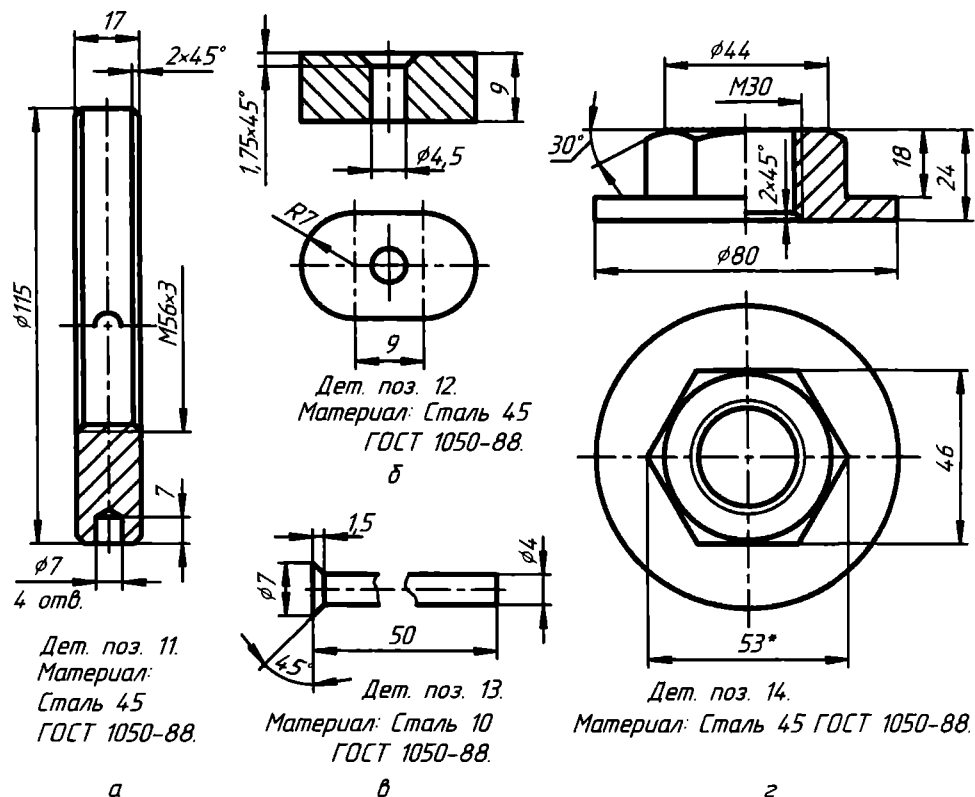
Чертежи: а — гаечного кольца; б — шпонки; в — заклепки; г — гайки
